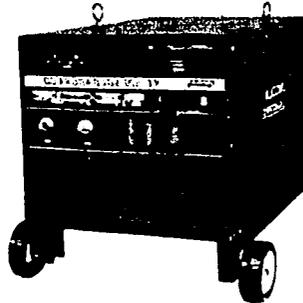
Máquina soldadora modelo RX-520 soldadora co. (Cortesía de SOMISA.)
